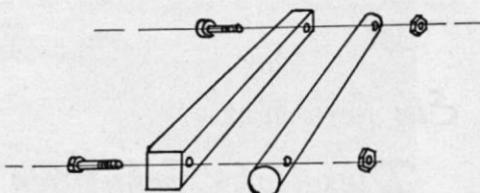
Die Einzelteile des Biegewerkzeugs.
